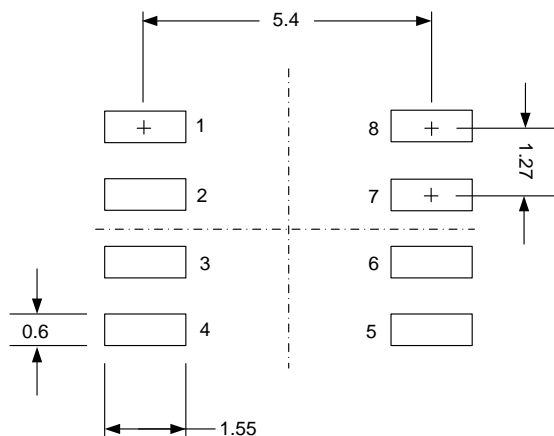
PCB 焊盘: 8-引脚 SOP
